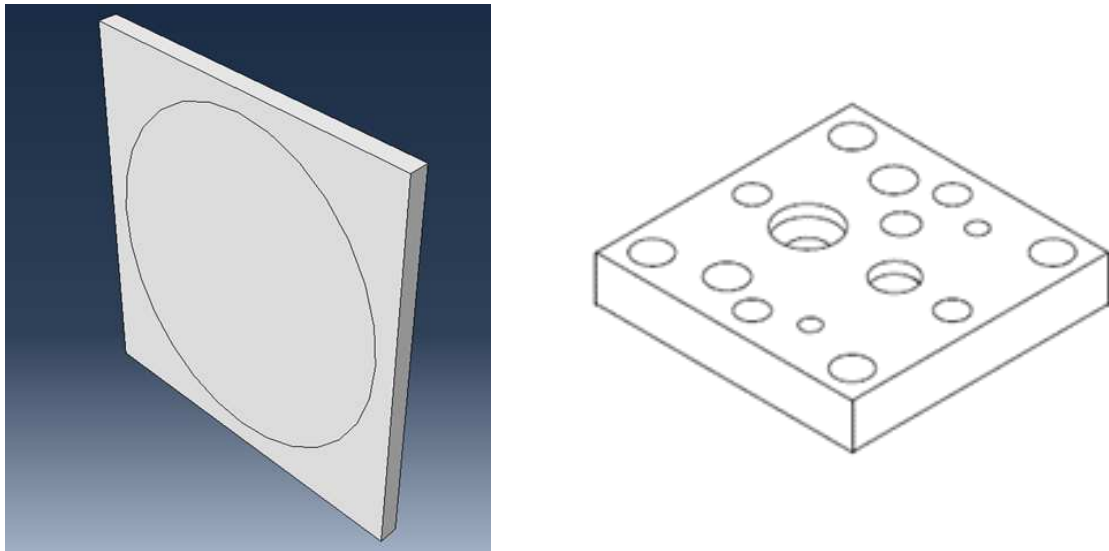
a) Primera aproximación a la geometría de la pieza. Geometría descartada; b) placa inferior para la fijación y guiado durante el taladrado de la muestra.
